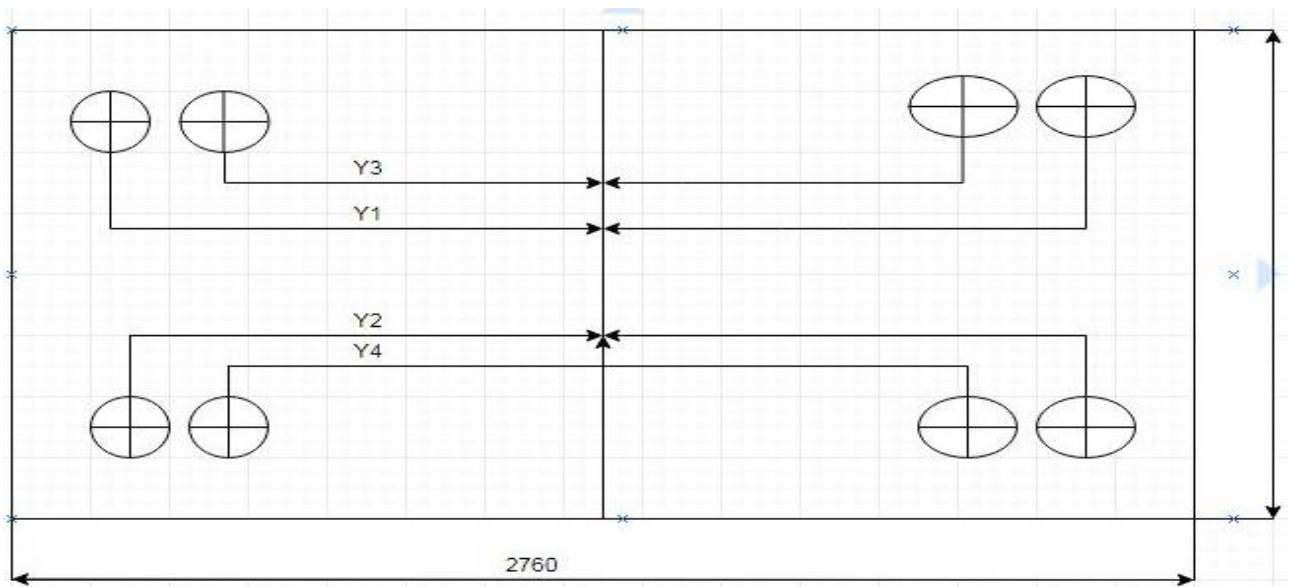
Схема кріплення рольганга-холодильника до фундаменту
